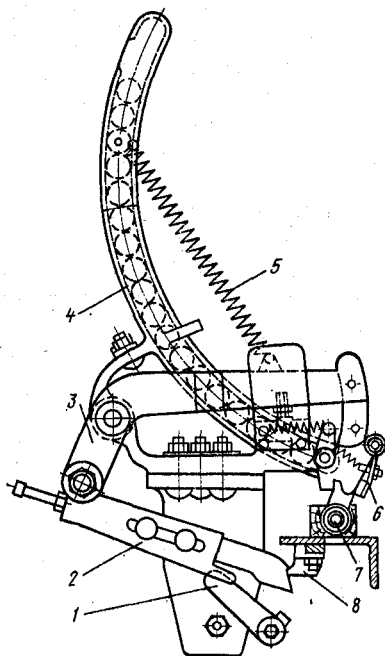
Схема механизма вкладки трубчатых початков станка АТ-120-ЛЗМ
